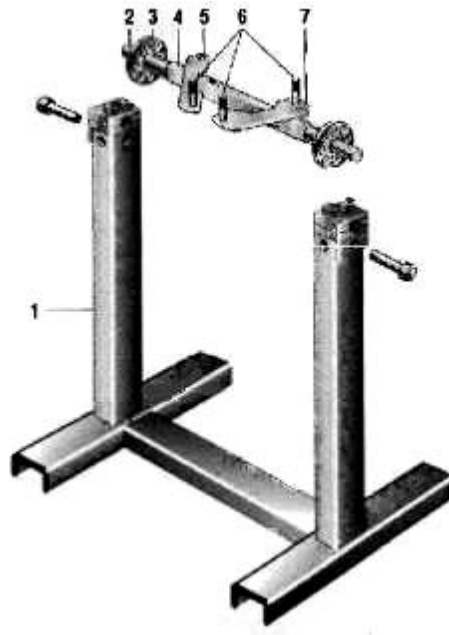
Траверса для коробки передач: 1 – універсальний стенд; 2 – цапфи; 3 – диск; 4 – траверса; 5 – ліва пластина; 6 – болт (3 шт.); 7 – права пластина; 8 – гайка шпильки коробки передач; 9 – гайка болта (6 шт.).
